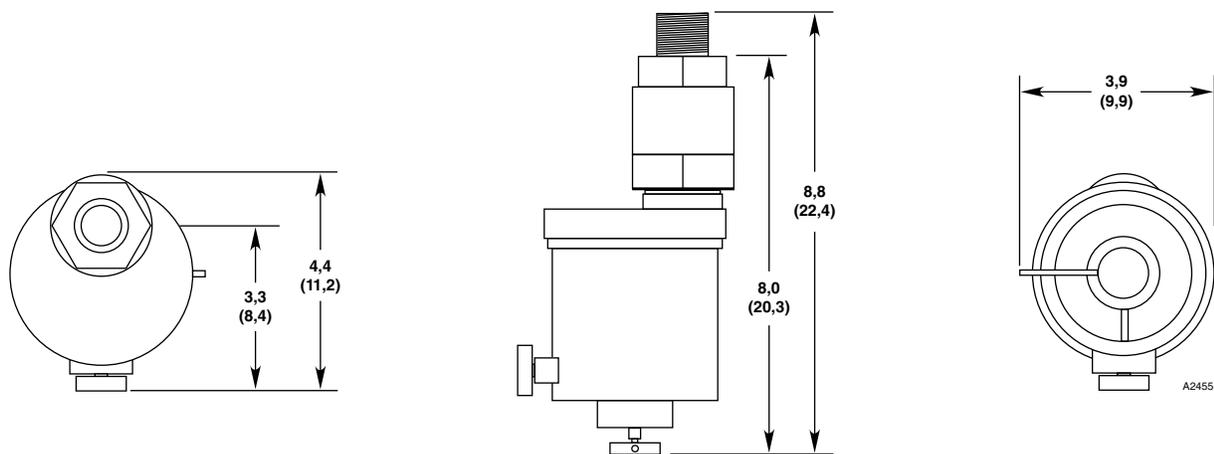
Dimensões do Detector NTMOS com Kit de Calibração de Ampola com Misturador Fixado em Polegadas (Centímetros)
